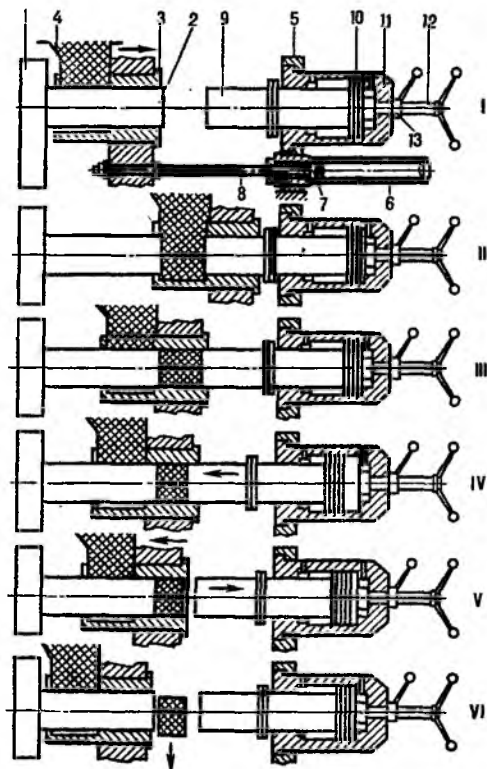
Схема гидравлич. таблеточной машины: I—начало цикла; II—загрузка перерабатываемого материала; III—перемещение материала в матрицу; IV—прессование; V—начало выталкивания таблетки; VI—сброс таблетки в тару; 1, 5—неподвижные шлиты; 2—неподвижный пуансон; 3—матрица; 4—бункер; 6—вспомогат. цилиндр; 7, 10—поршни; 8—тяга; 9—подвижный пуансон; 11—рабочий цилиндр; 12—винт; 13—контргайка.
